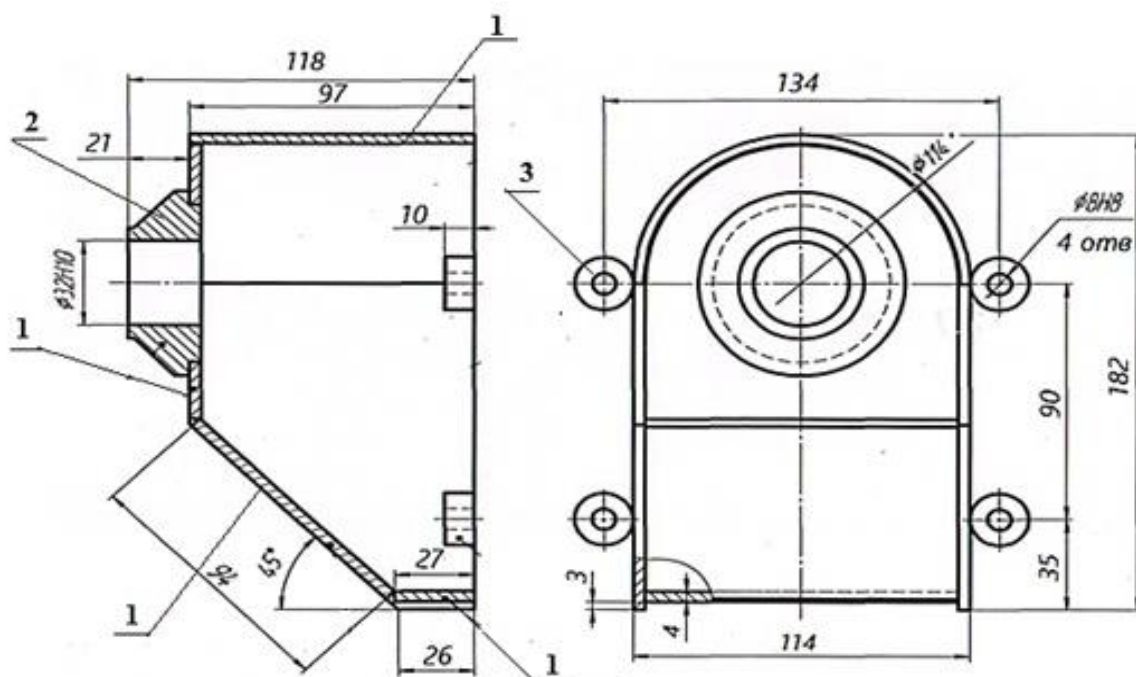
Конструкция вспомогательного корпуса перфоратора
